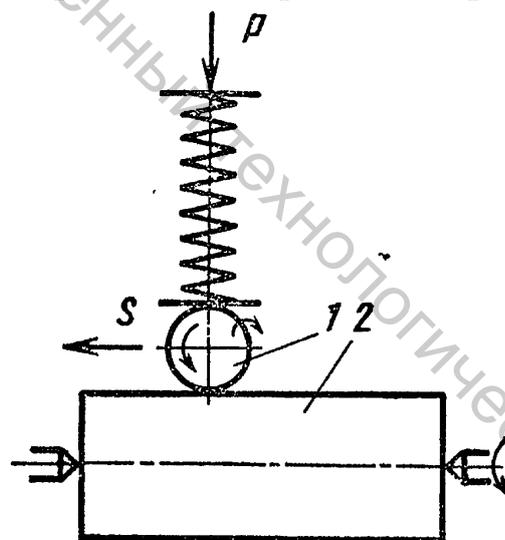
Схема упрочняюще-чистовой обработки – обкатывание шаром (ОШР): 1 – шар; 2 – обрабатываемая деталь
